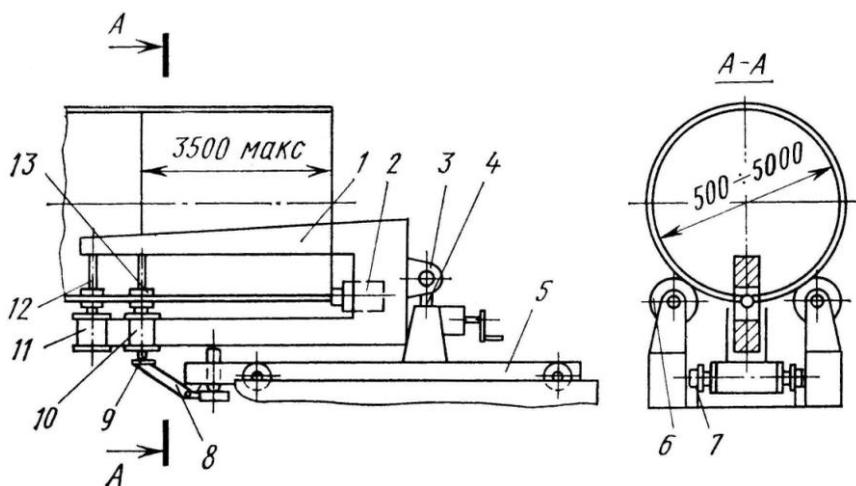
Скоба для сборки кольцевых стыков обечаек:
